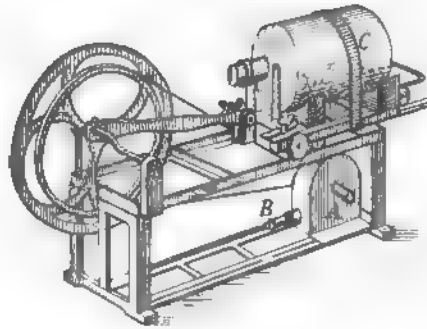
Schüttelmaschine mit Turbinenantrieb.
